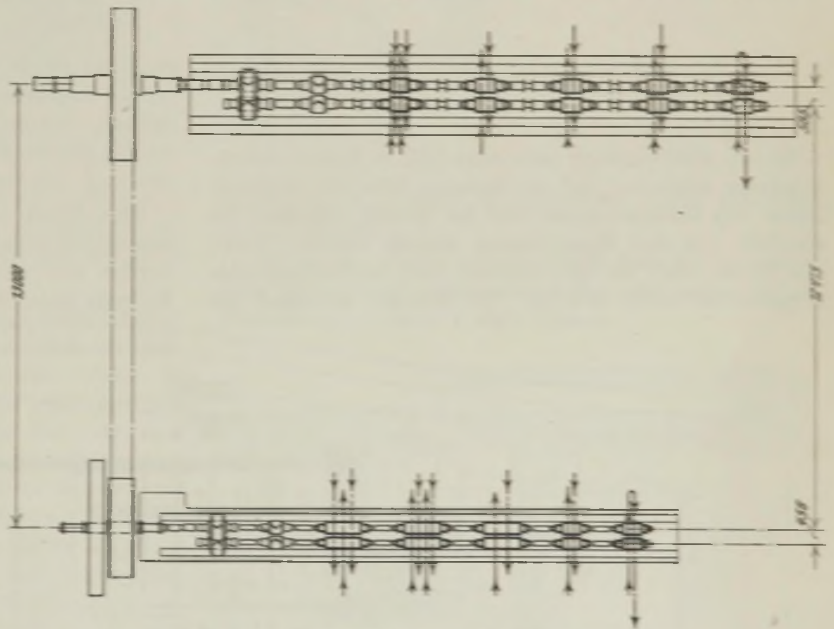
Grundriß der 350/450er Walzenstraße.
